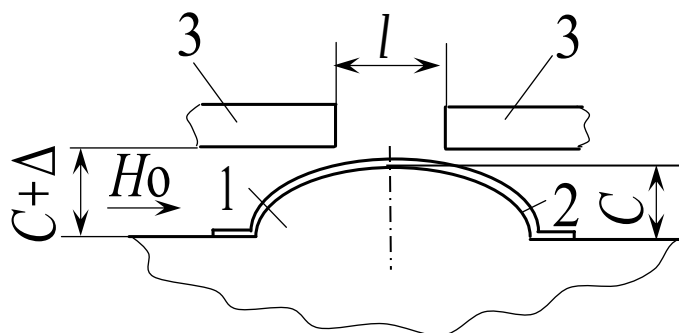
Вид и расположение КМИ при осуществлении способа магнитографического контроля [8]: 1 – контролируемый сварной шов; 2 – магнитная лента; 3 – концентраторы магнитной индукции
